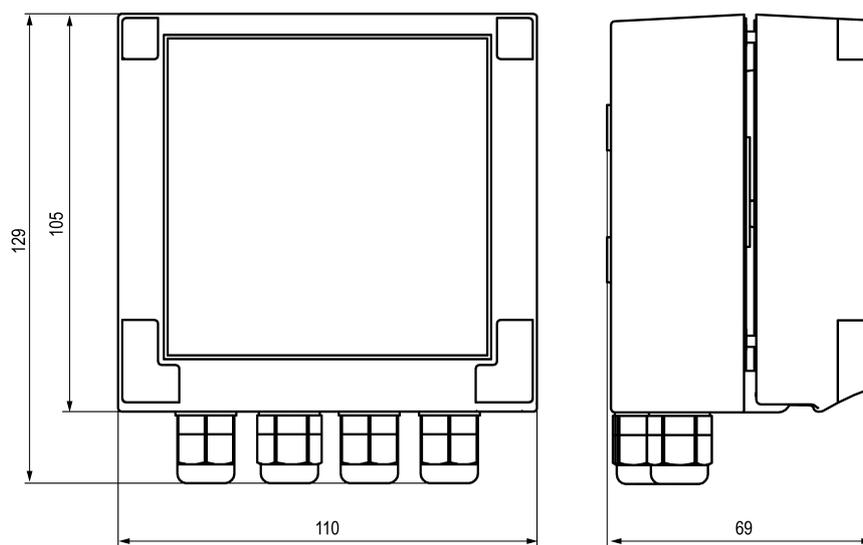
Габаритные размеры прибора в корпусе Н
